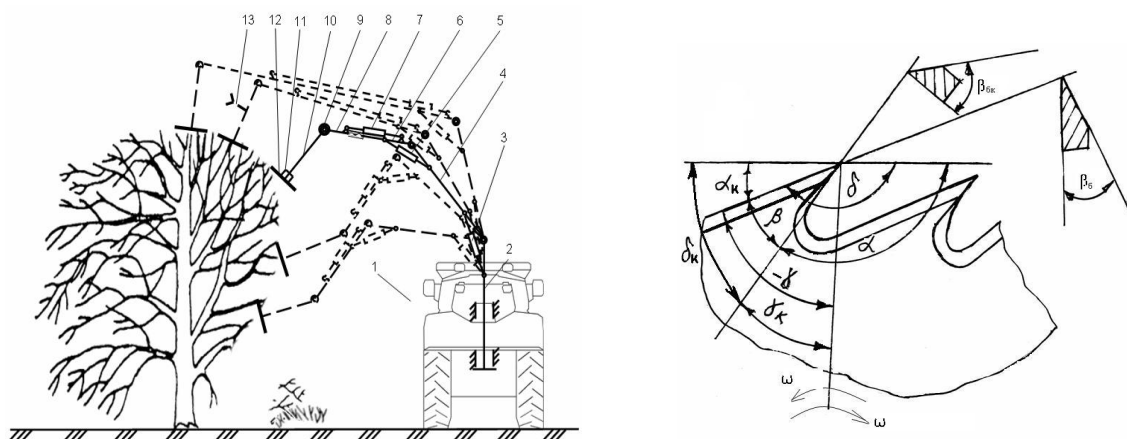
Схема машины для обрезки крон деревьев: 1 – базовая машина; 2 – поворотная колонна; 3 – гидроцилиндр стрелы; 4 – стрела; 5 – гидроцилиндр рукояти; 6 – рукоять; 7 – гидроцилиндр удлинителя; 8 – удлинитель рукояти с винтовой парой; 9 – гидродвигатель (ротатор); 10 – маятниковый рычаг; 11 – гидромотор пилы; 12 – дисковая пила; 13 – V-образный упор.
